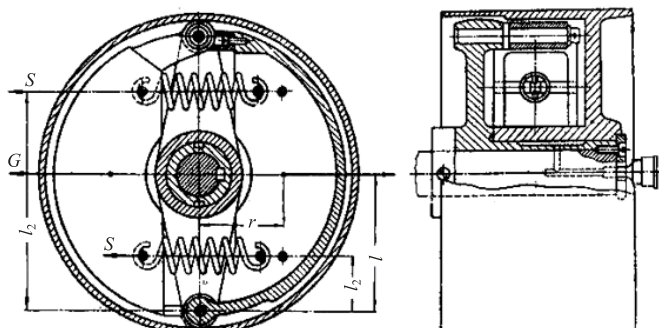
Муфта с поворотными колодками, шарнирно соединенными с полумуфтой и со свободными колодками, поставленными в крестовину
